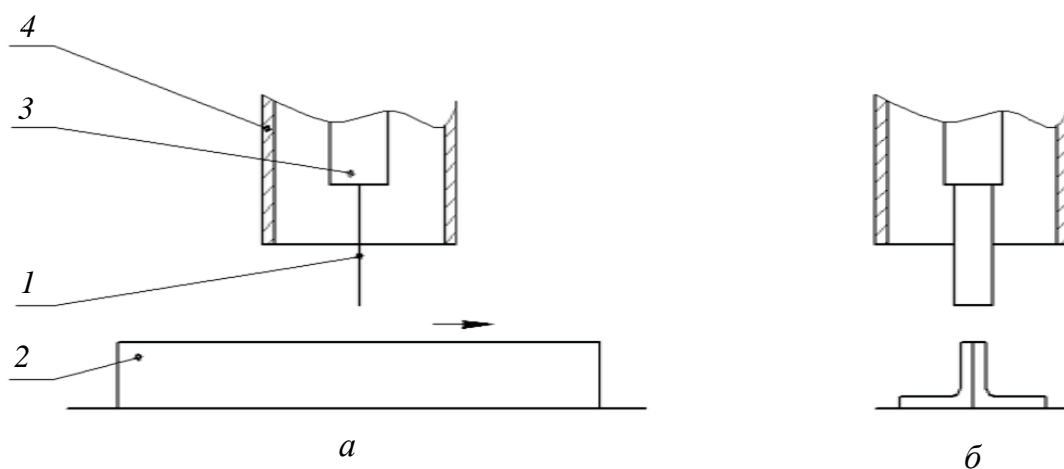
Схема сварки образца по отбортовке: *а* – вид спереди, *б* – вид сбоку. 1 – плоский электрод; 2 – образец; 3 – цанга; 4 – сопло
